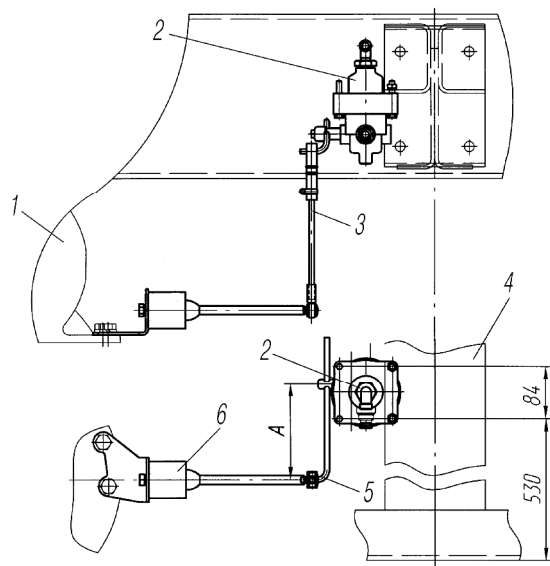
Установка регулятора тормозных сил: 1- мост средний; 2- регулятор тормозных сил (РТС); 3- тяга регулировочная; 4- поперечина № 5; 5- рычаг РТС; 6- элемент упругий РТС; А- длина рычага РТС
